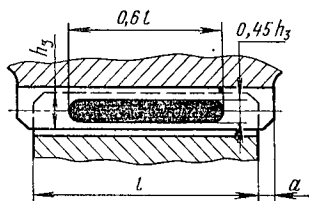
Пятно контакта ведомой цилиндрической шестерни
